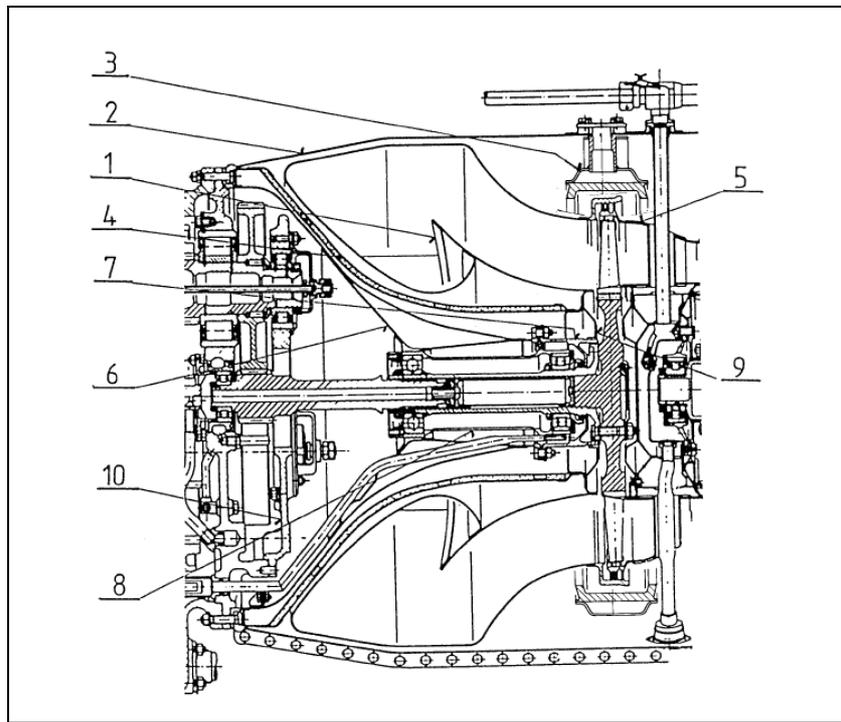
il *PT shaft* ed il *quill shaft* all'interno del *supporting cone*, tra *power turbine* e *reduction gearbox* (ingrandimento).
